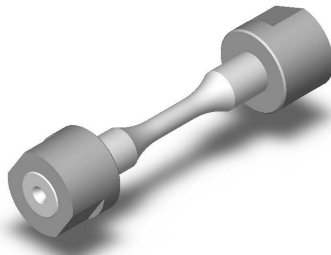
Aufbau Gewindeprobe mit Adapterhülsen.
